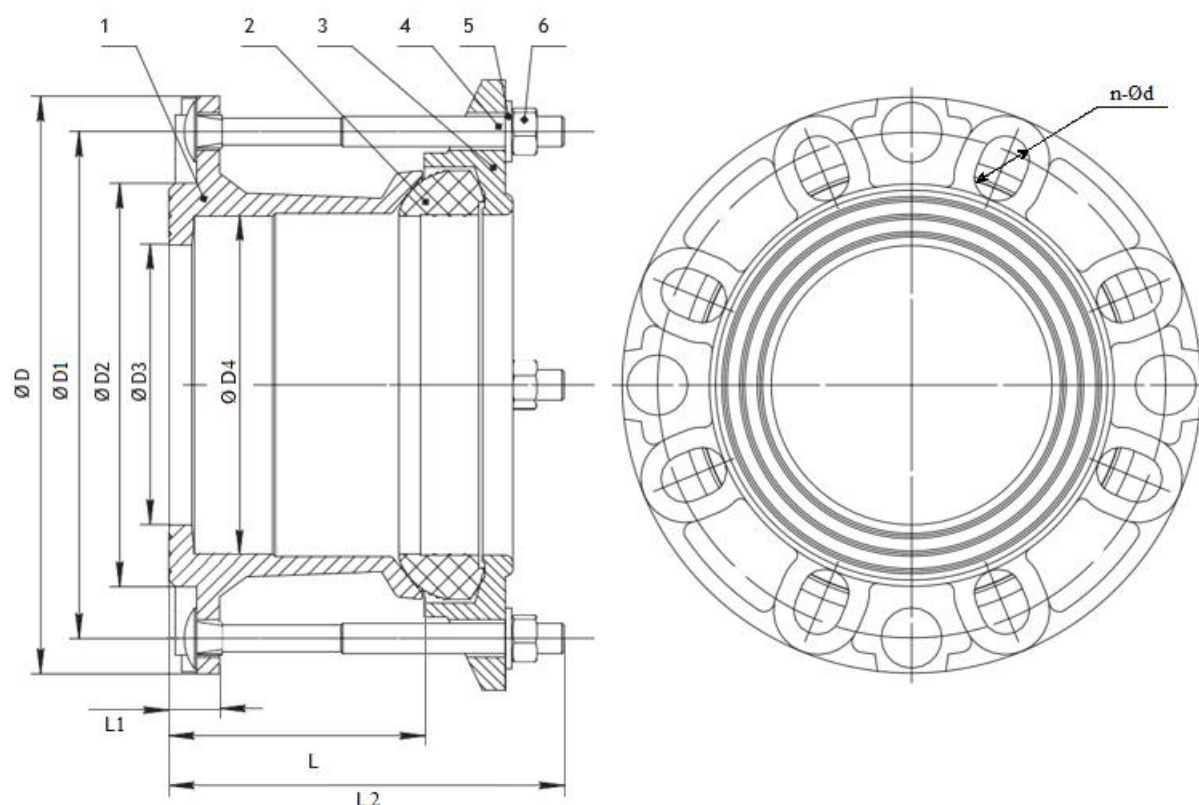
Фланец обжимной универсальный FA-U13.J DN50-700 PN16 и фланец обжимной FA-U13.J FIX DN800-2000 PN10, PN16
